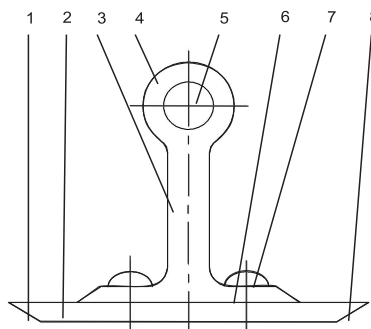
Т-подібний ніж різальних апаратів з горизонтальними осями обертання робочих органів: 1, 8 — різальна кромка; 2 — різальна пластина; 3 — планка; 4 — вушко; 5 — отвір; 6 — поперечина; 7 — заклепка
